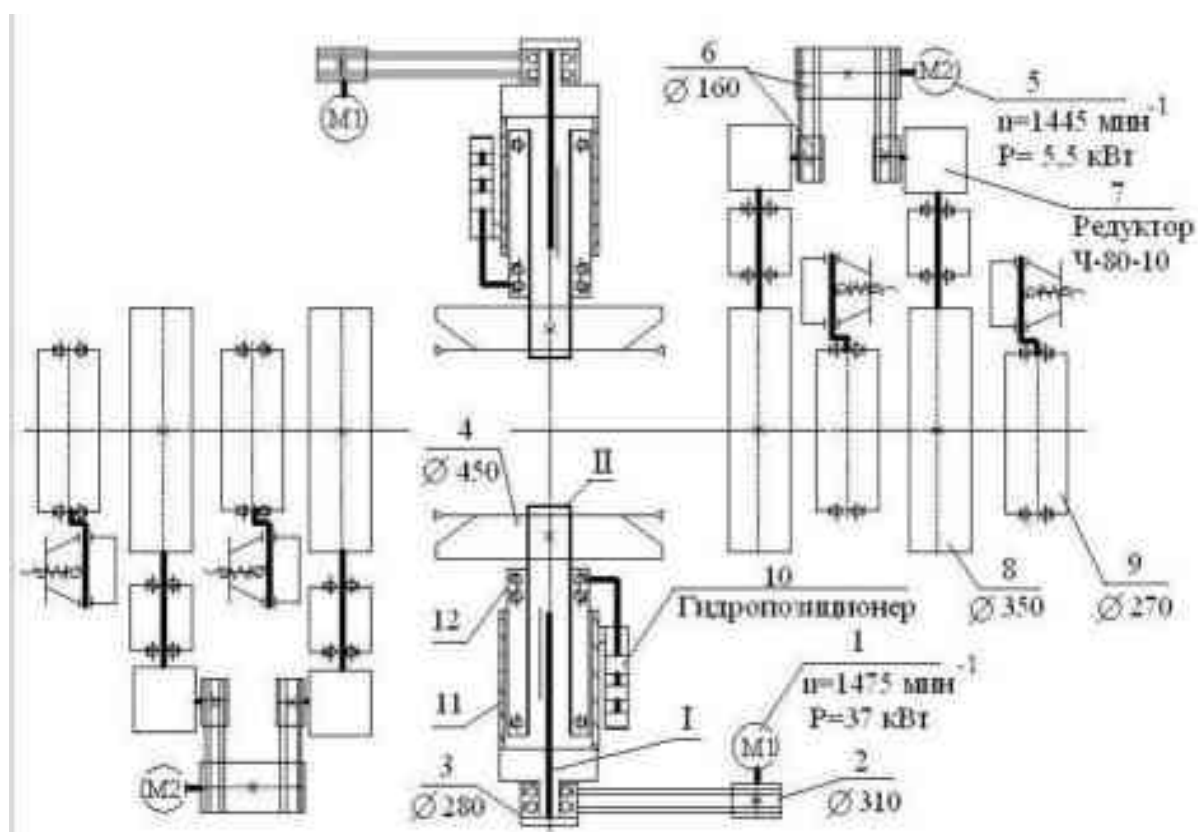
Кинематическая схема станка Ц2Д-1Ф
